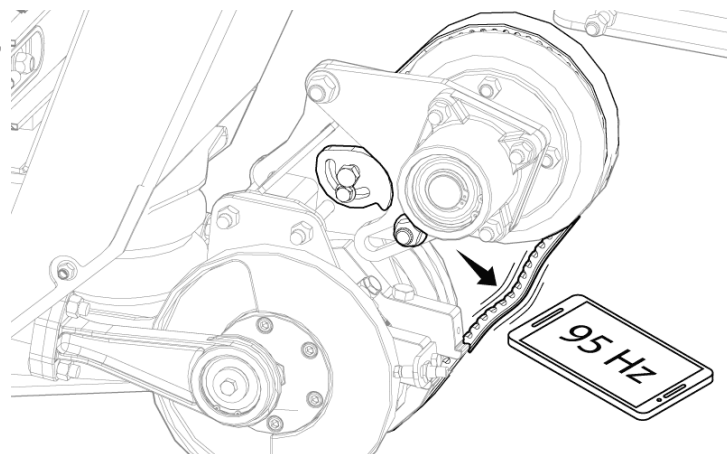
«Пощипывание» ремня и проверка натяжения.
